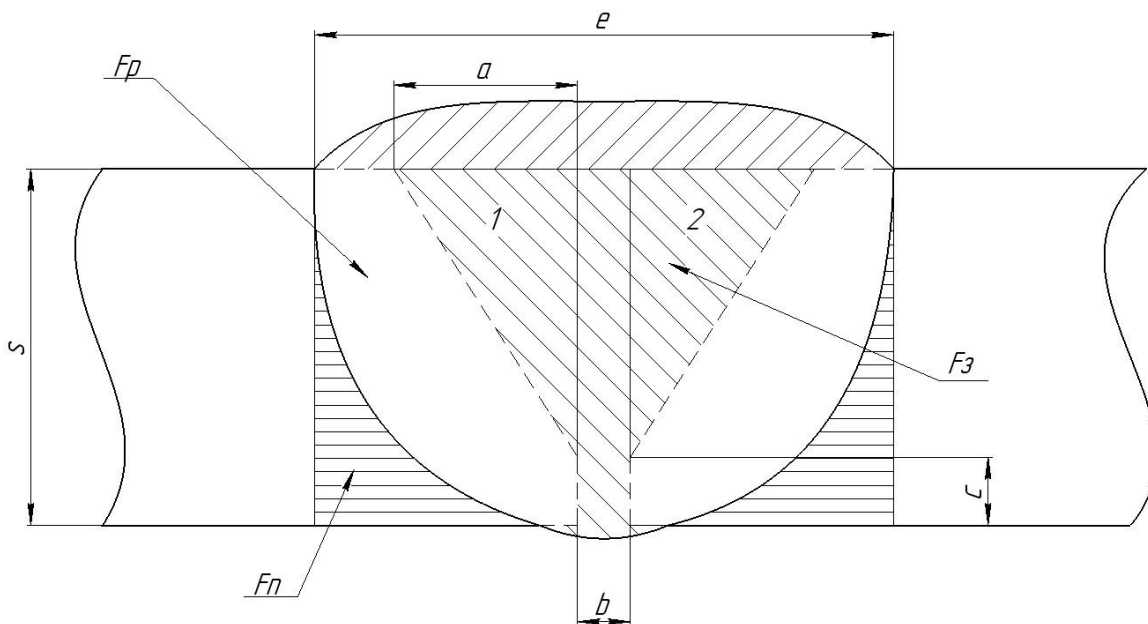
Схема для расчета параметров режима при стыковой механизированной сварке в защитных газах по ГОСТ 14771-76 с V-образной разделкой кромок с притуплением
